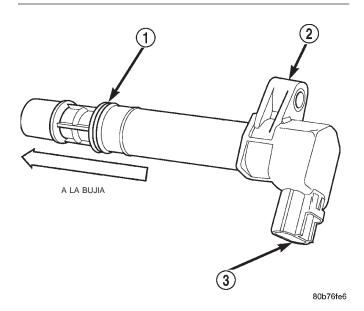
BOBINA DE ENCENDIDO - 3.7L
